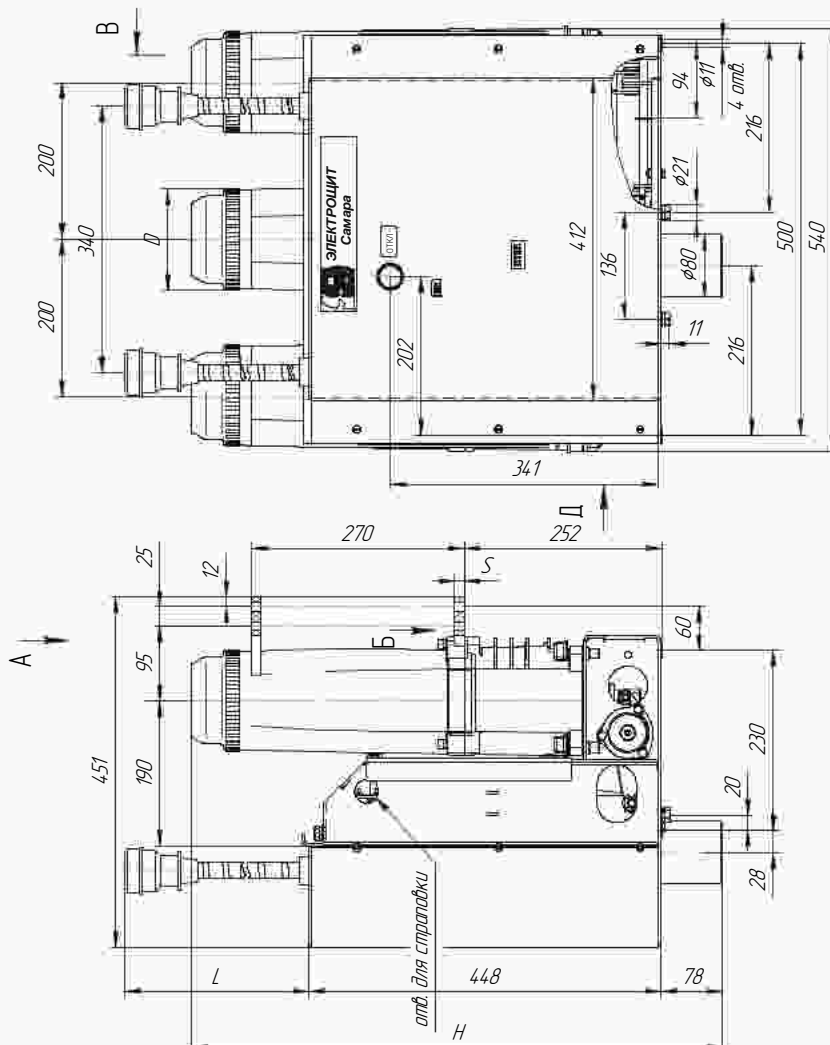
Габаритные, присоединительные и установочные размеры выключателя типа ВВУ-СЭЩ-Э3-10-20(31,5)/
